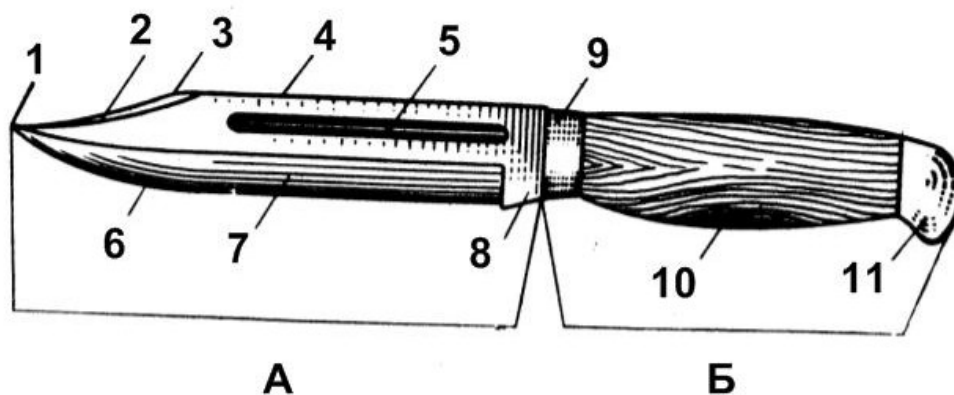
Нож: А) клинок, Б) рукоятка: 1) острие; 2) заточка скоса обуха; 3) скос обуха; 4) обух; 5) дол; 6) лезвие; 7) заточка лезвия; 8) пятка клинка; 9) соединительное кольцо; 10) ручка; 11) наконечник
